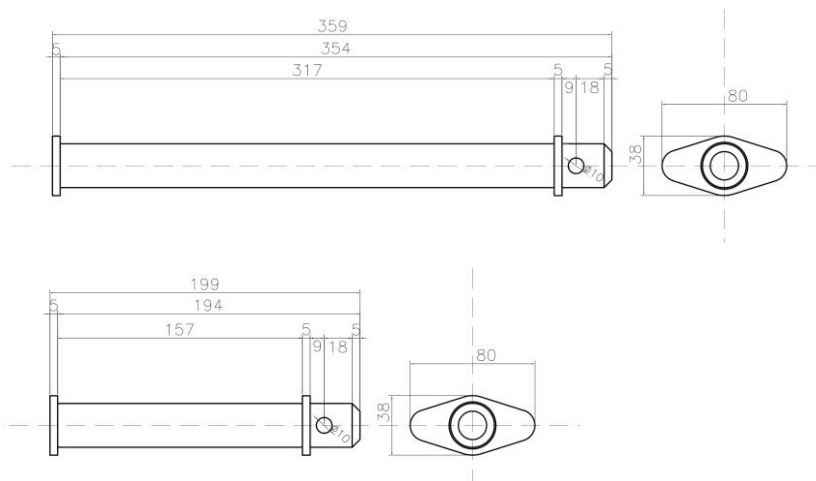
Bulones y arandelas para las fijaciones de las piezas de conexión.
